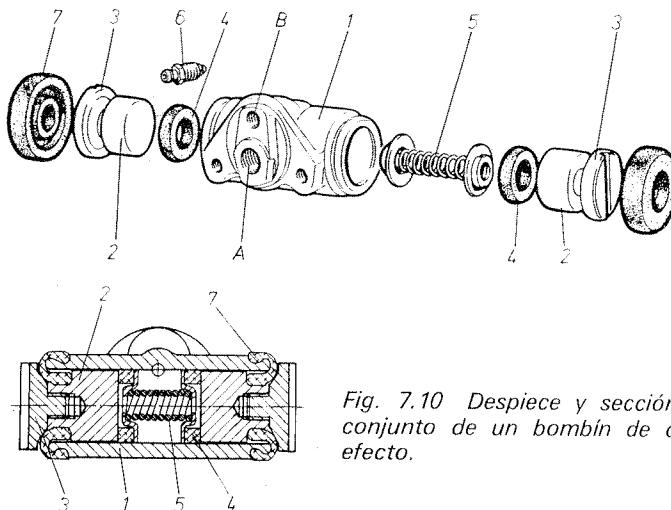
Despiece y sección del conjunto de un bombín de doble efecto.
